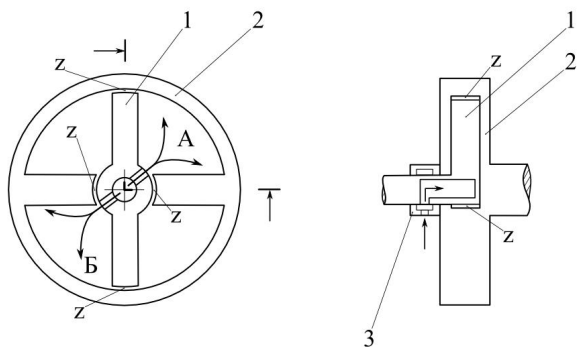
Схема вращающегося гидроцилиндра: 1 – вал с лопатками; 2 – корпус с лопатками; 3 – система подачи рабочей жидкости
